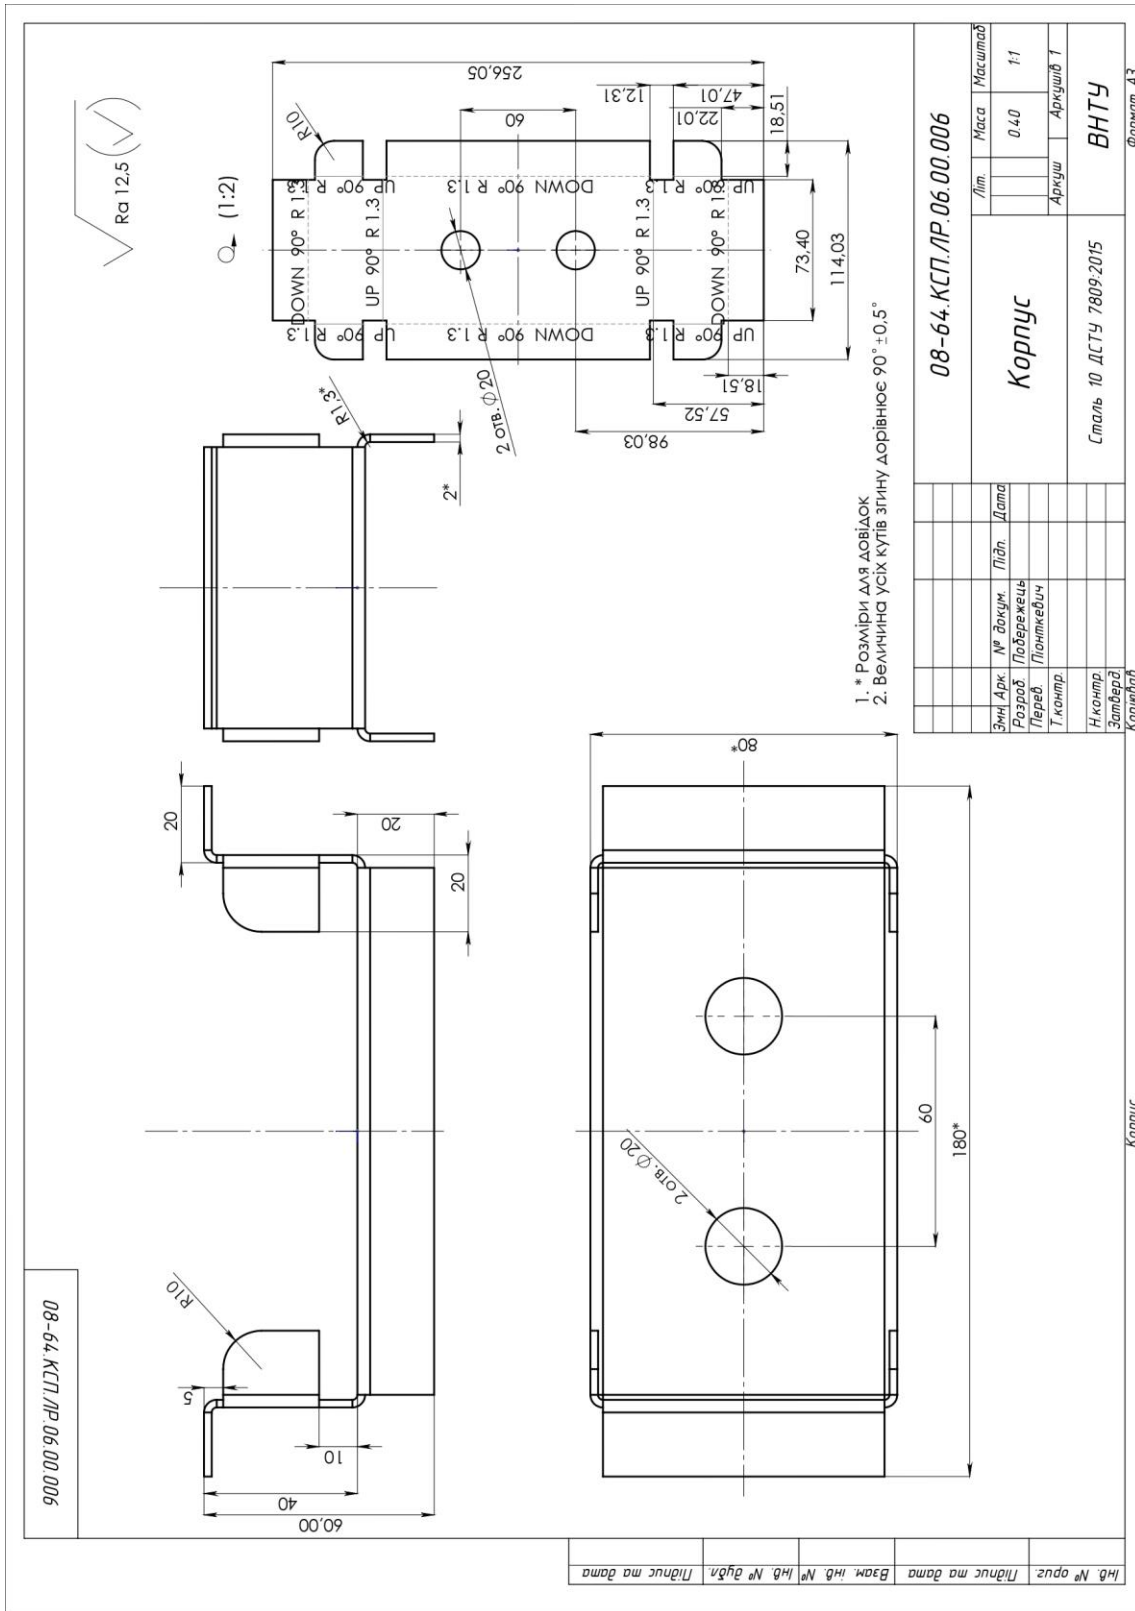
Асоціативний креслення деталі «Корпус»
